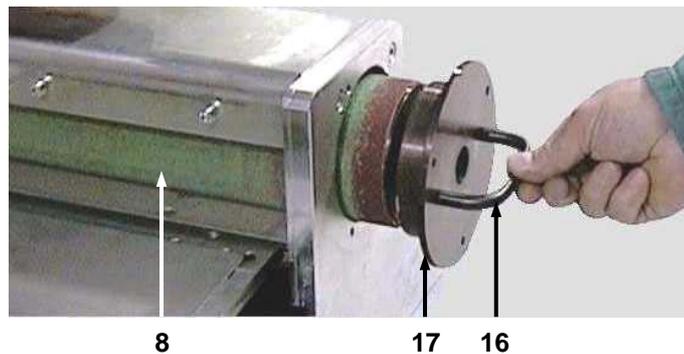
DESMONTAJE DEL RODILLO DE BISELADO
